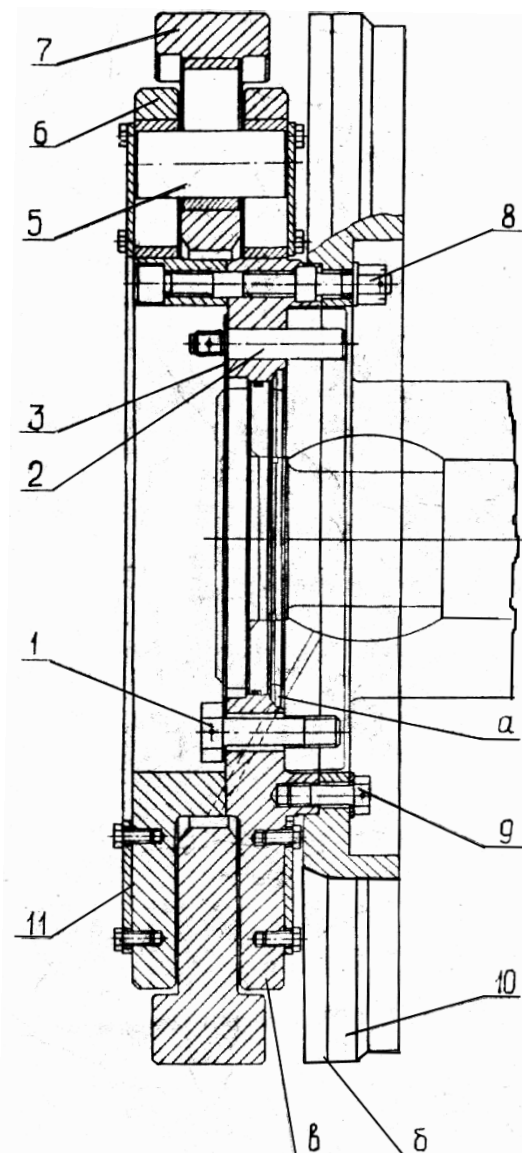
Антивибратор комбинированный: 1, 9 – болты; 2 – штифт; 3 – пластина замочная; 8 – гайка; 5 – палец; 6 – ступица; 7 – маятник; 10 – демпфер; 11 – крышка; а – кольцевая полость для смазки; б – соединение крышки с корпусом; в – поверхность расположения отверстия под ремонтный болт
